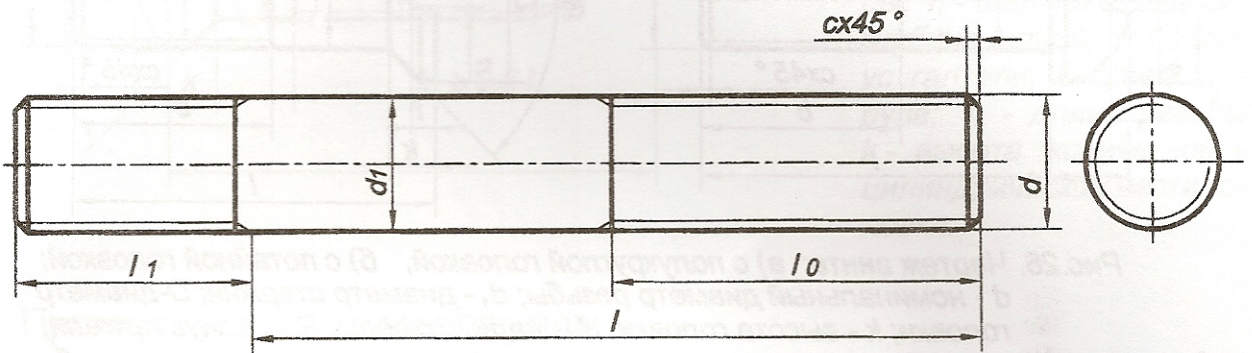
Чертеж шпильки: d - номинальный диаметр резьбы; l_1 - длина ввинчиваемого (посадочного) конца; l_0 - длина гаечного (стяжного) конца; l - длина шпильки; $с$ - фаска; d_1 - диаметр стержня
